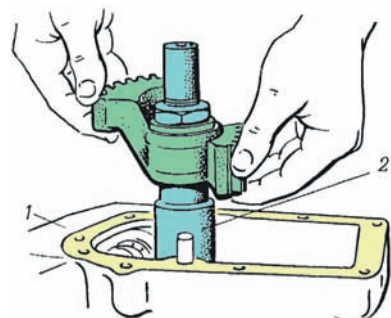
Снятие поворотного вала: 1 — корпус ГУРа; 2 — поворотный вал с сектором.
